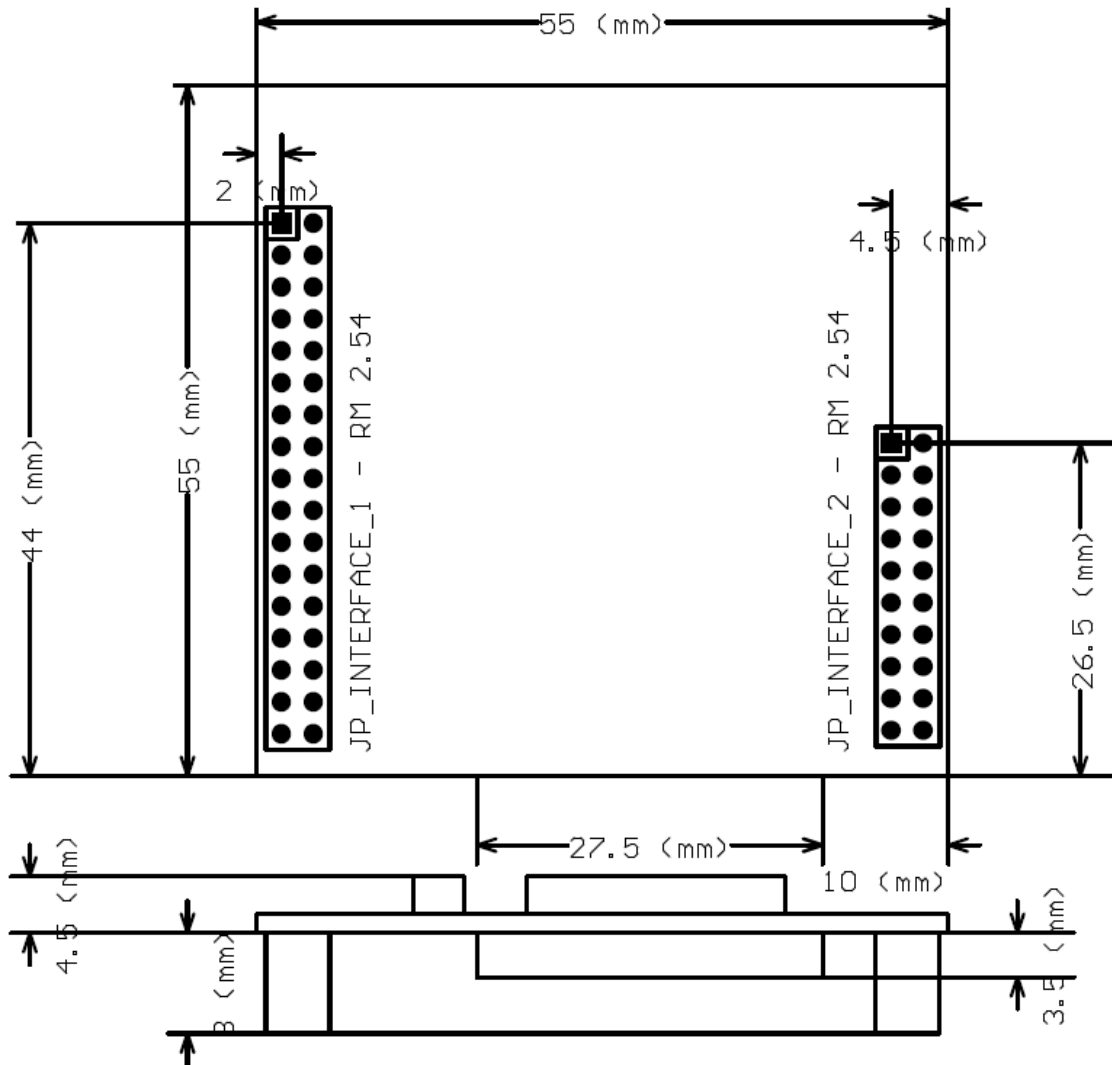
Fallguy ULTRA MP3 Modul Rev.E - Abmessungen
